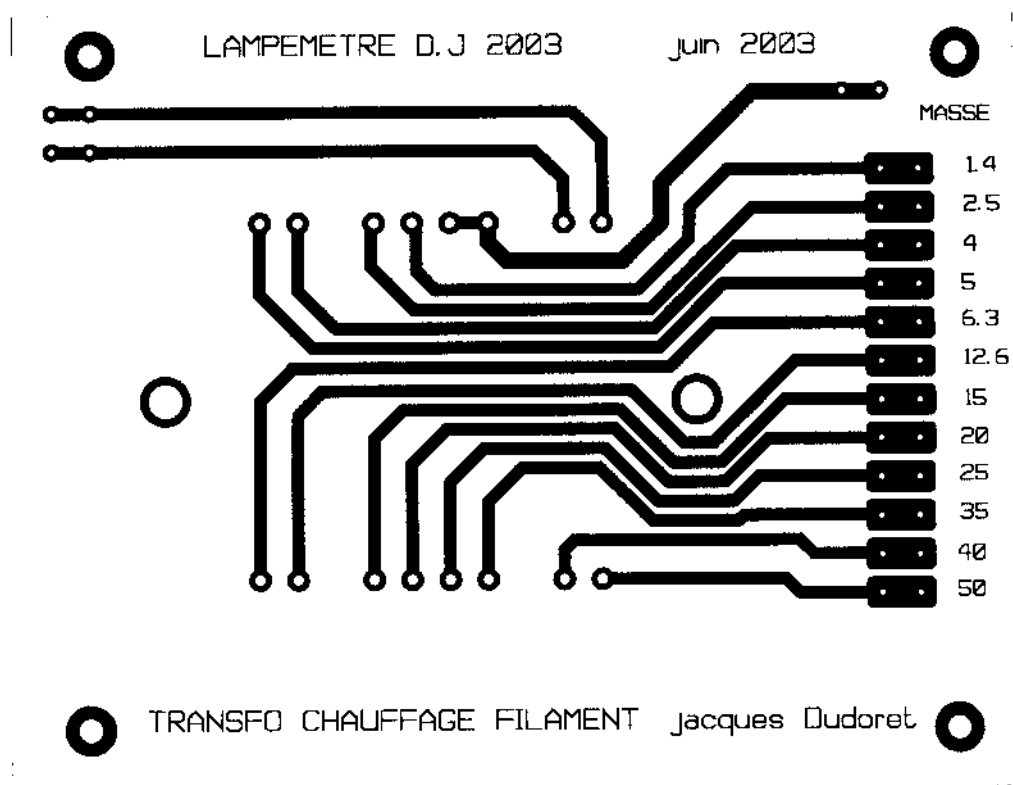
circuit imprimé chauffage filament coté soudures.
